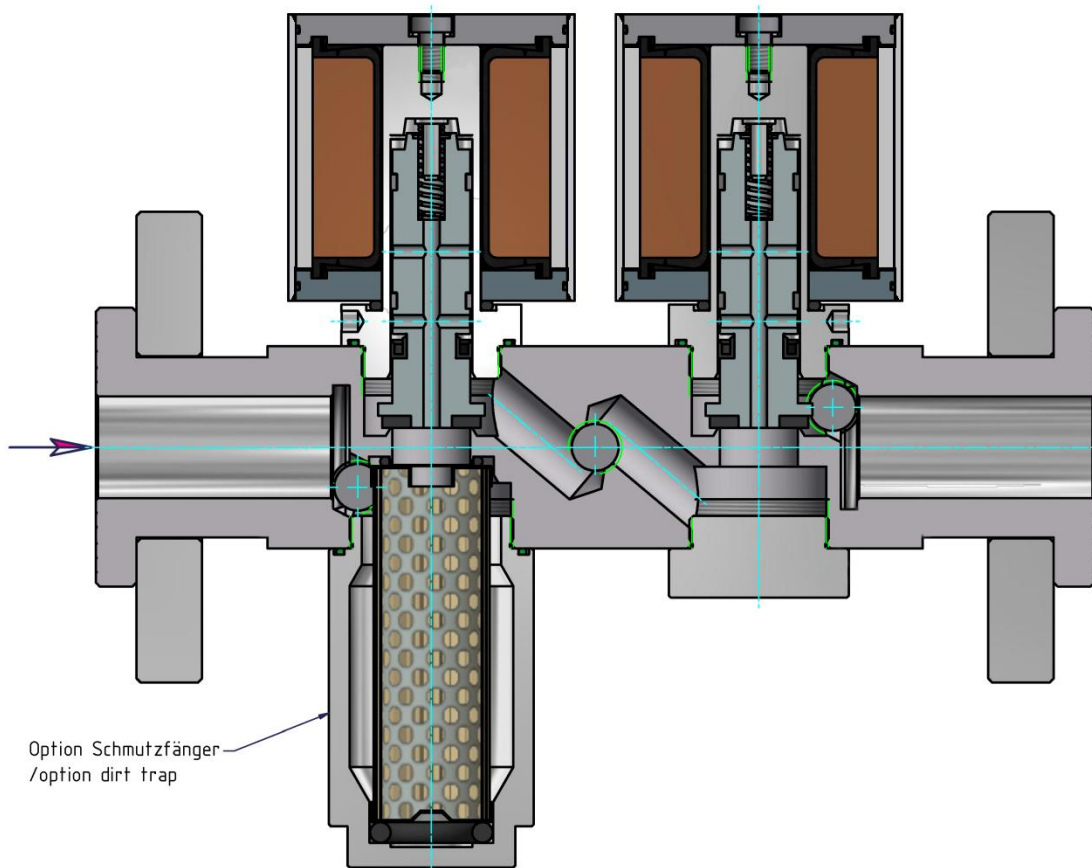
Gewindeausführung DVS... mit Schmutzfänger (116.002.295)
